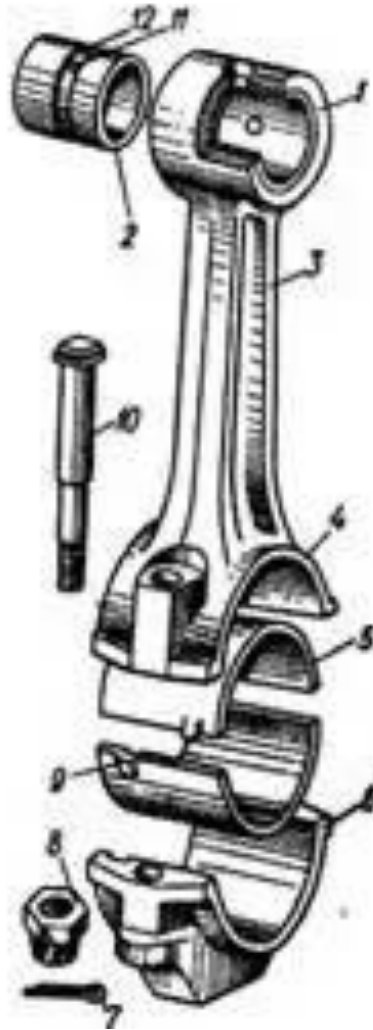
Шатун і шатунні підшипники: 1 – верхня головка; 2 - втулка верхньої головки; 3 - стержень; 4 - нижня головка; 5 - вкладиш шатунного підшипника; 6 - кришка нижньої головки; 7 – шплінт; 8 – гайка; 9 - вус-фіксатор; 10 - шатунний
